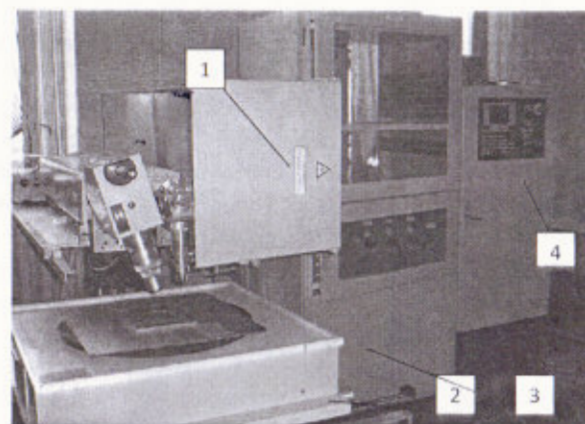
Экспериментальная установка, общий вид 1 – защитный кожух; 2 – координатный стол; 3 – силовой шкаф; 4 – ЧПУ SINUMERIC 802S
